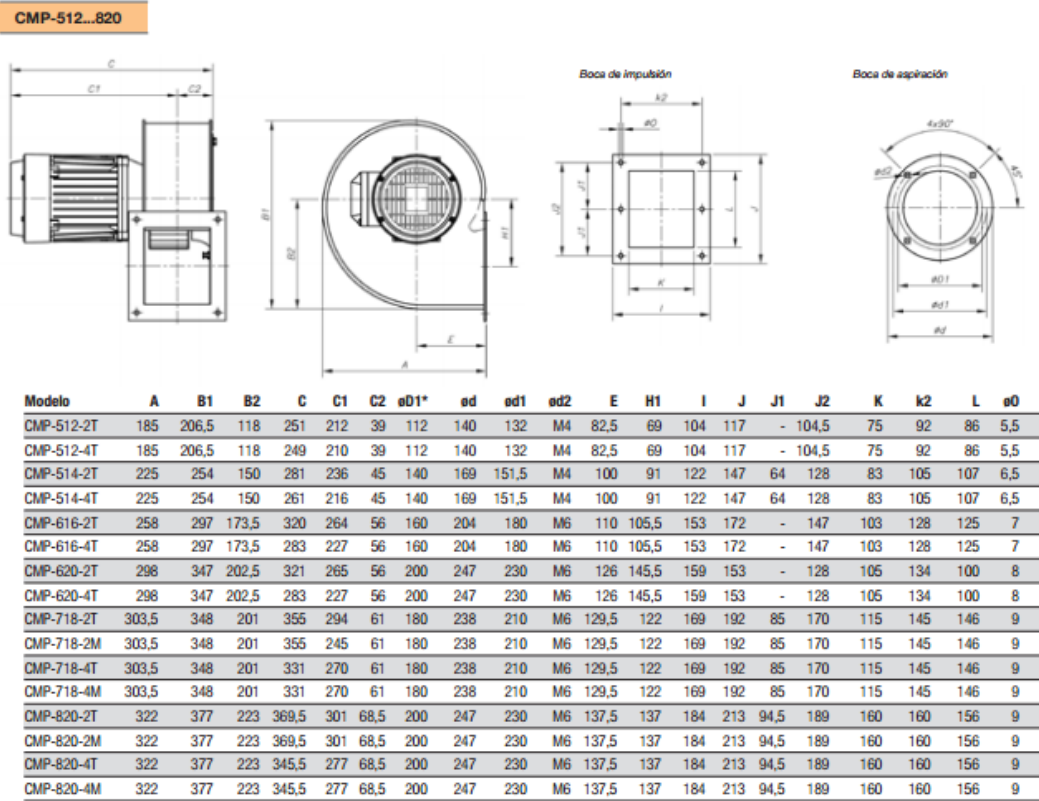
Dimensiones, Línea Sodeca CMP A.
